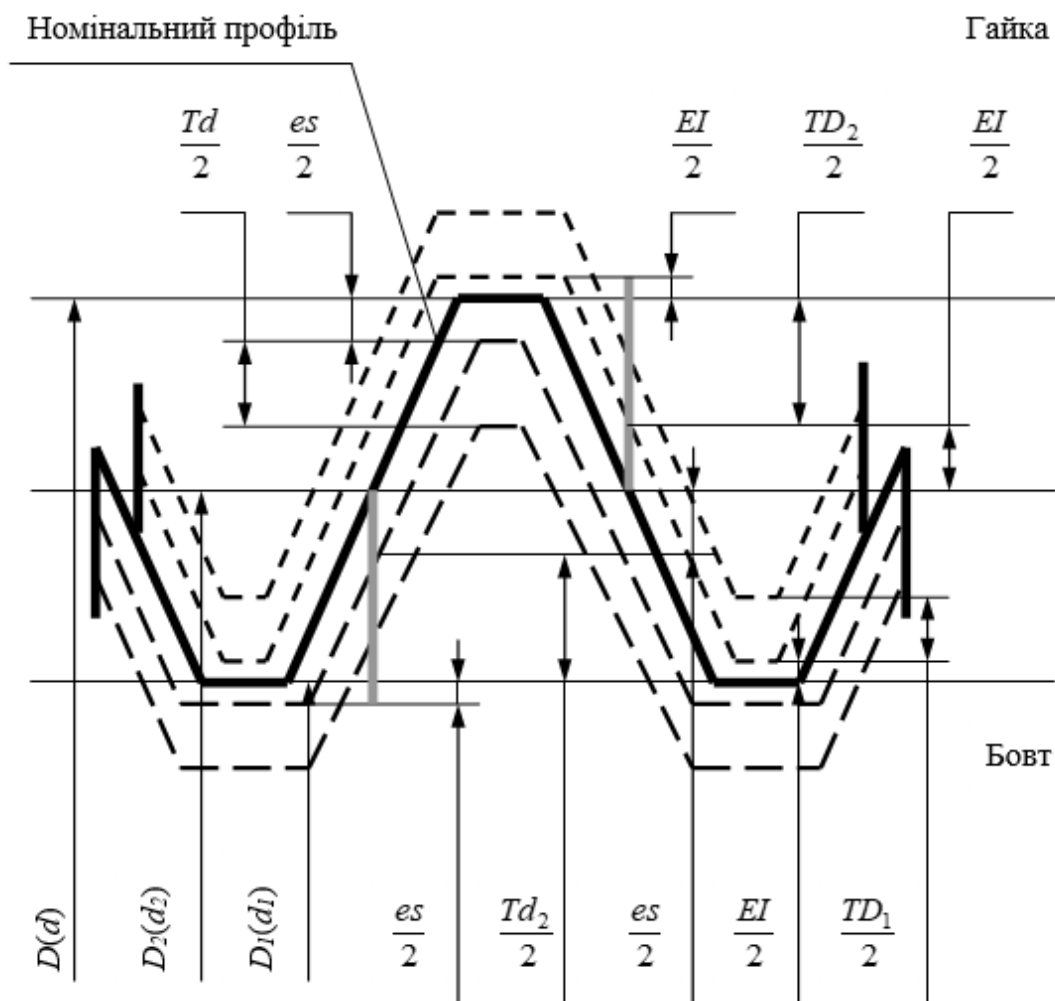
Схема посадки метричного різьбового з'єднання із зазором
